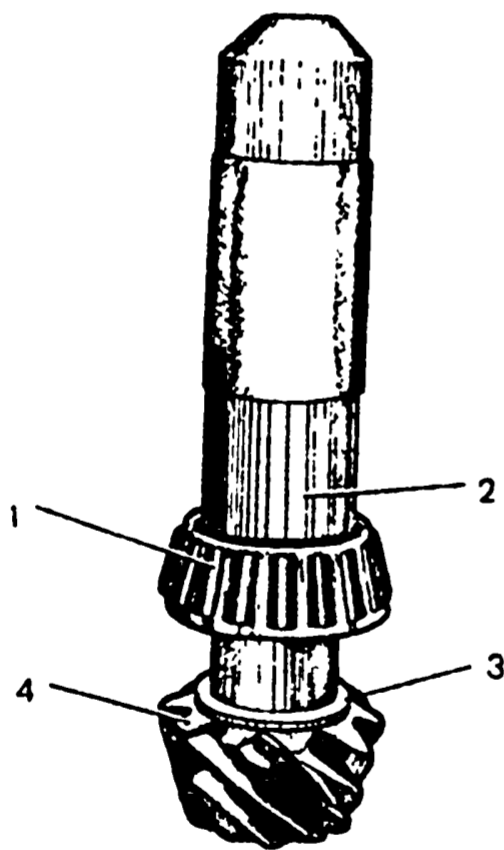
Установка внутреннего кольца заднего подшипника на ведущую шестерню: 1 - внутреннее кольцо заднего роликоподшипника; 2 - оправка А.70152; 3 - регулировочное кольцо; 4 - ведущая шестерня
